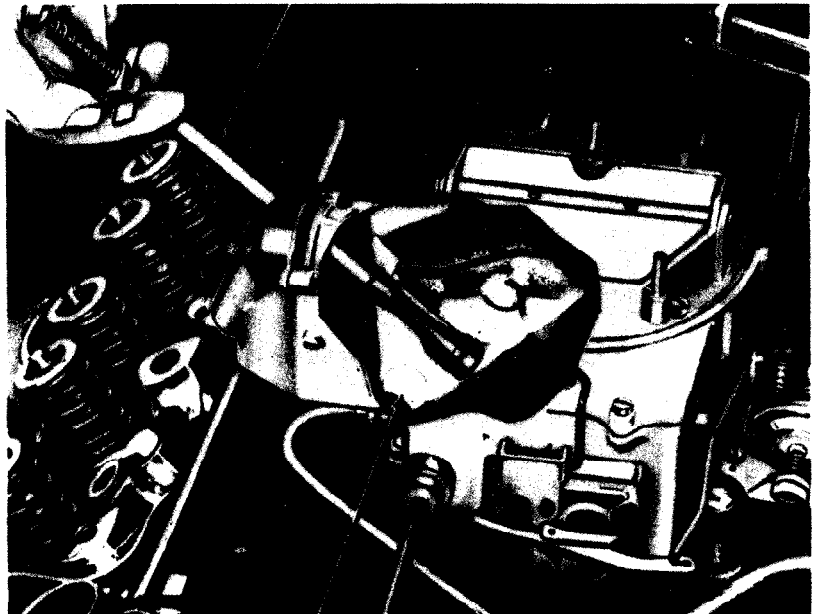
Desmontaje de un taqué, por medio de una herramienta magnética especial (*Ford Division of Ford Motor Company*).
